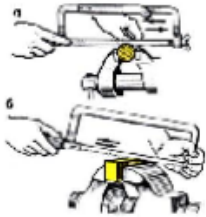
Начало резки ножовкой металла: а - круглого, б – квадратного
